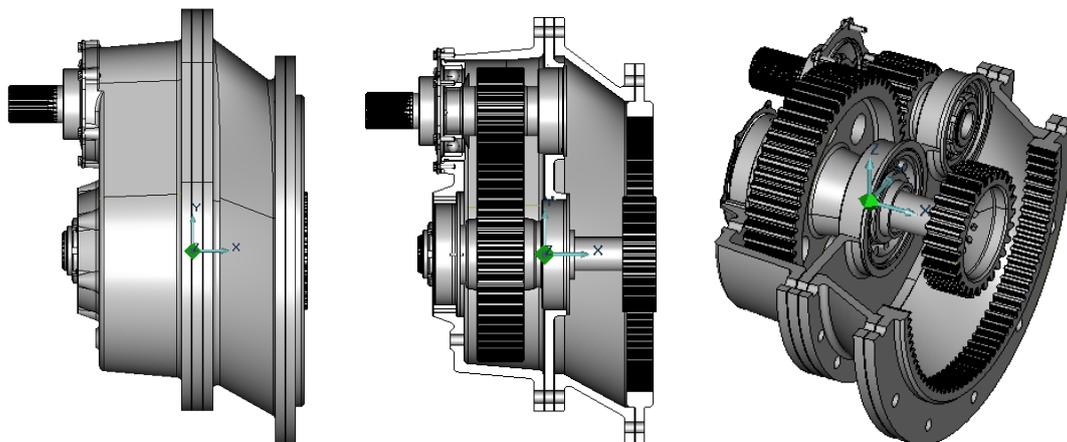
Модели нижнего, верхнего и среднего корпусов редуктора
